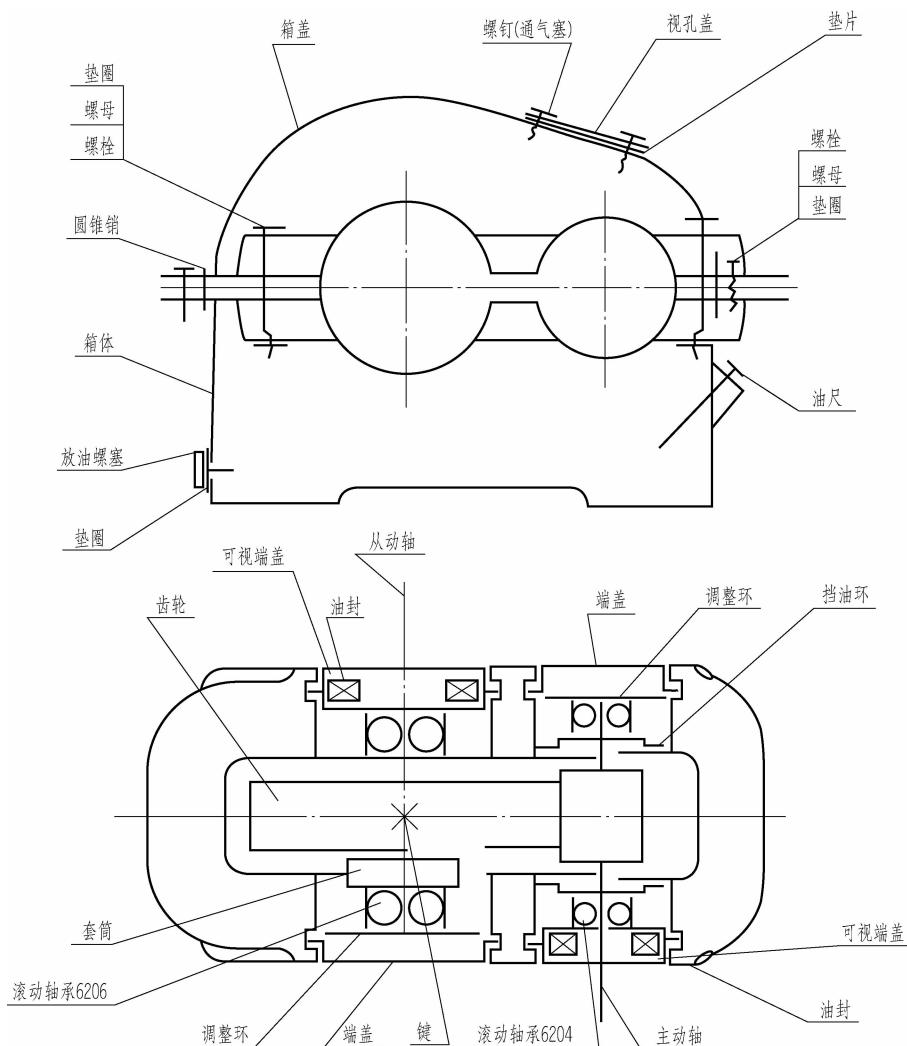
一级直齿圆柱齿轮减速器的装配示意图
